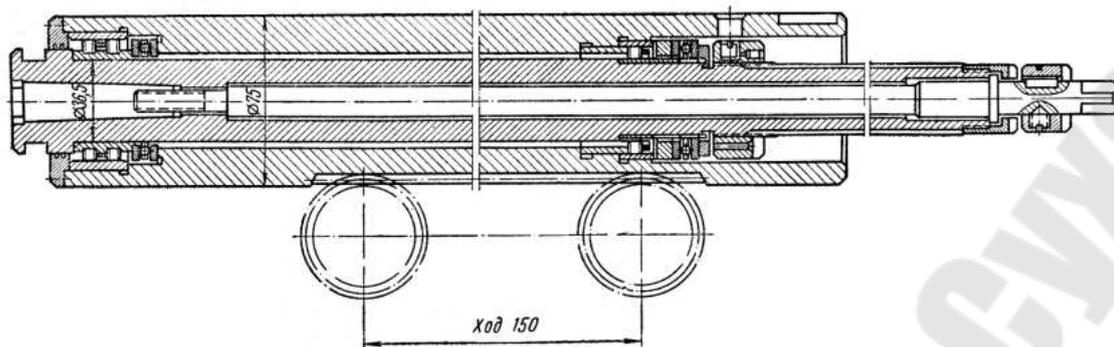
Шпиндель координатно-расточного станка 2А430
